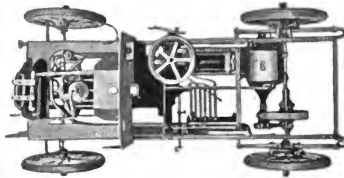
Chassis von Champroberts Wagen „Electrogénia“. Draufsicht.
